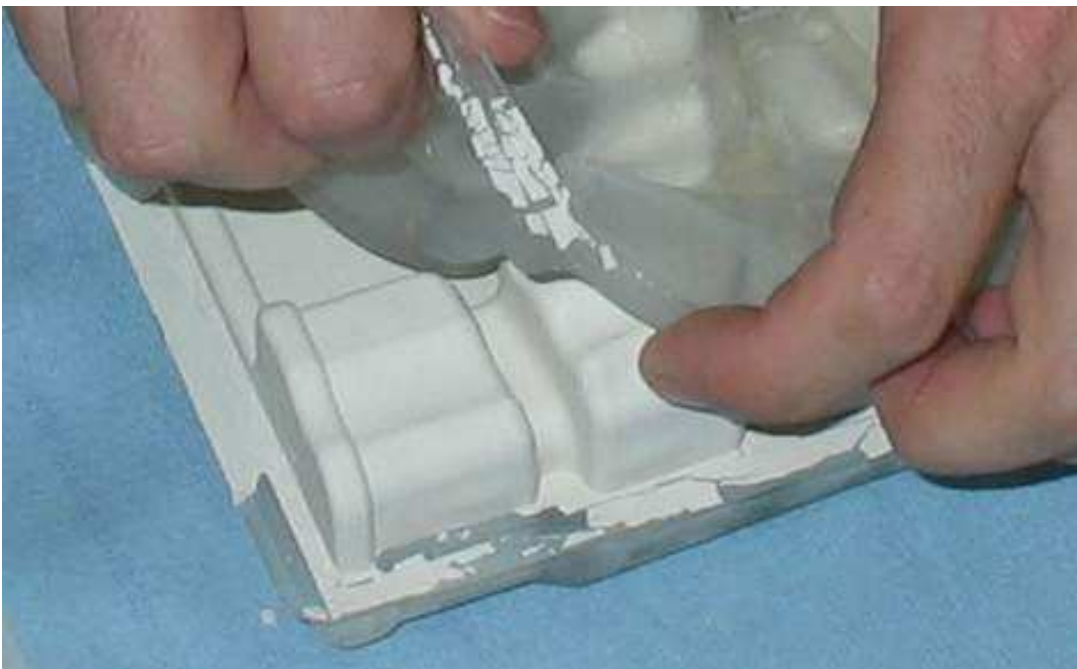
Werkzeug und Abformmodell für Turbinenschaufelkern
